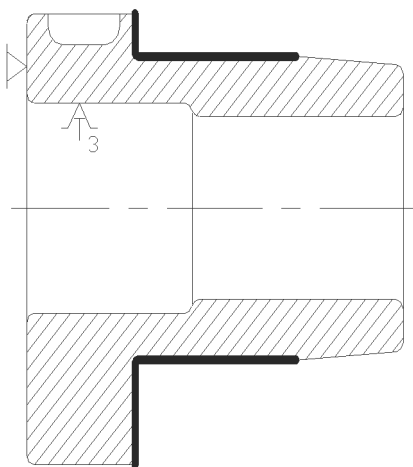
Ескіз чорнової бази деталі „Циліндрична втулка”
